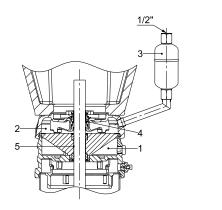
CR 120 und 150 mit luftgekühlter Wellendichtungskammer
